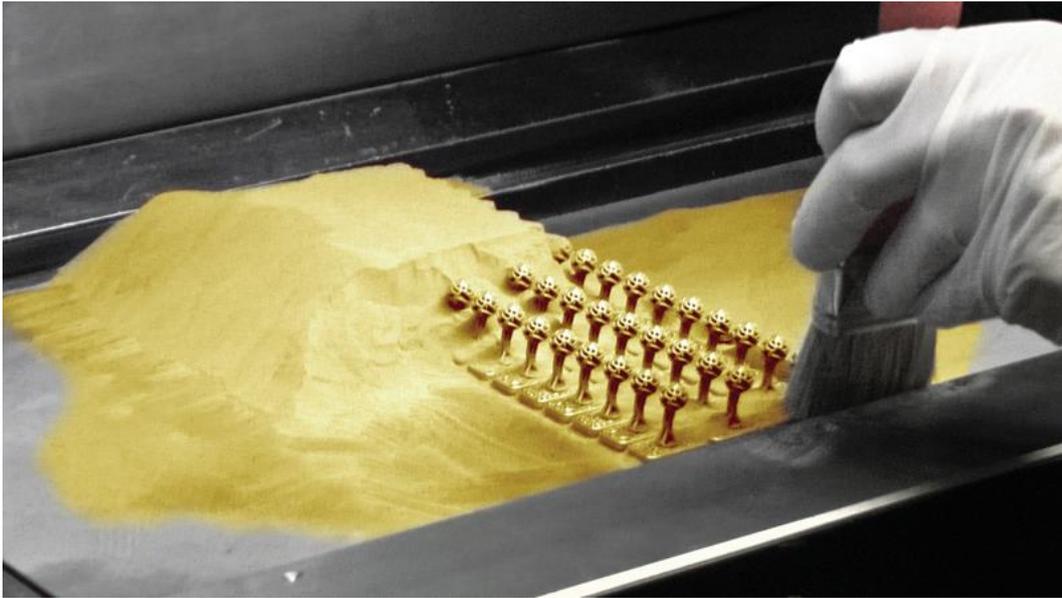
Etapas e técnicas para construção do molde, fundição, separação e limpeza das joias.
